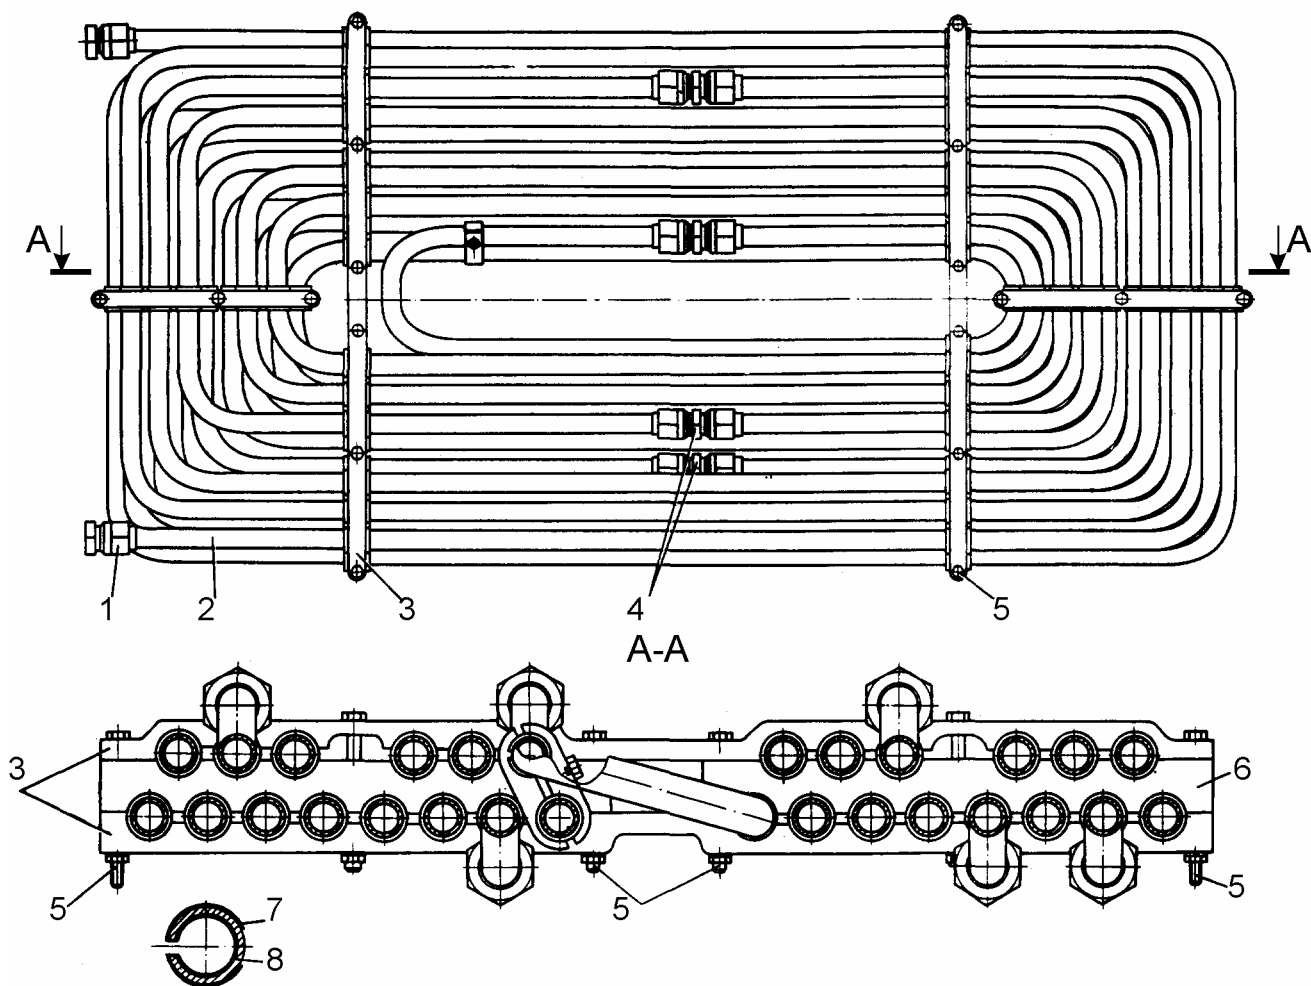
Паливорідинний теплообмінник, розташований у витратному баці (Ан-124): 1 — накідна гайка; 2 — труба; 3 — колодка; 4 — штуцери; 5 — болти; 6 — вкладиш; 7 — стрічка металізації; 8 — втулка
